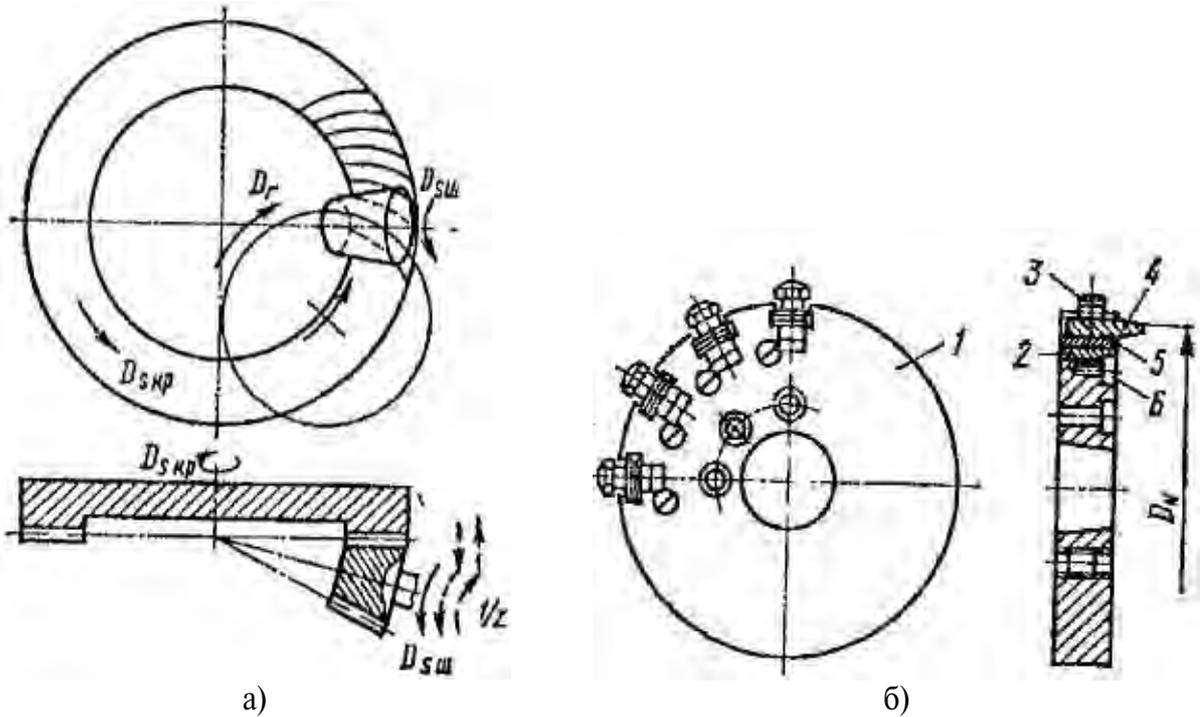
Изготовление конического колеса с криволинейными зубьями:
